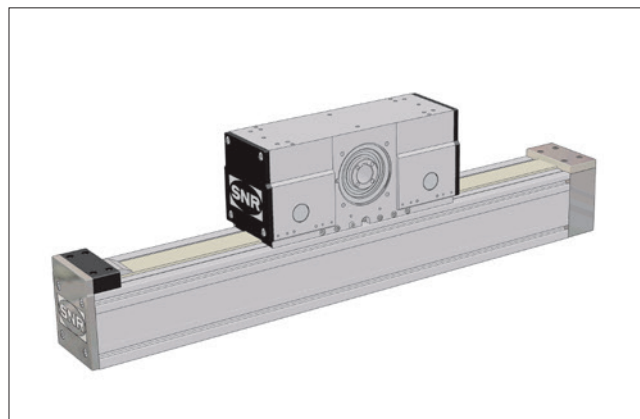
AXC mit Zahnriemen - Ω - Antrieb
